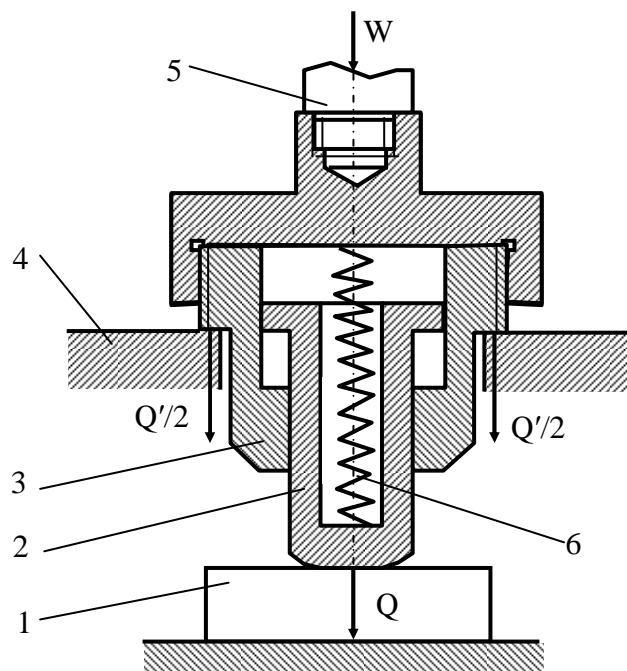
Схема пружинного притискача: 1-заготовка; 2-стакан; 3-корпус; 4-упор; 5-шток силового приводу; 6-пружина.
